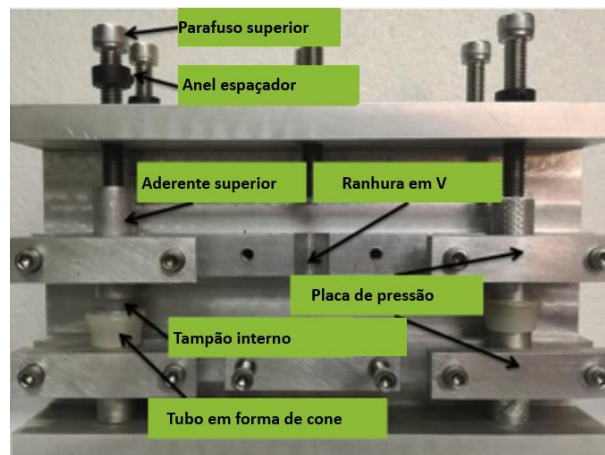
Molde utilizado por Jun Zhang et al. para fabricação de juntas topo a topo, adaptado de [20]
